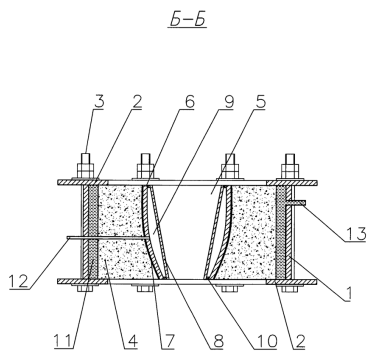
Взрывная камера, вид Б-Б [6], где: 1 – металлический наружный корпус в форме цилиндра; 2 и 3 – верхние и нижние упорные кольца; 4 – силовой элемент; 5 – рабочая полость; 6 – вставка; 7 – компенсационная прокладка; 8 – заготовка; 9 – вакуумная плоскость; 11 – гидравлическая камера; 12 – вакуумная трубка; 13 – штуцер.
